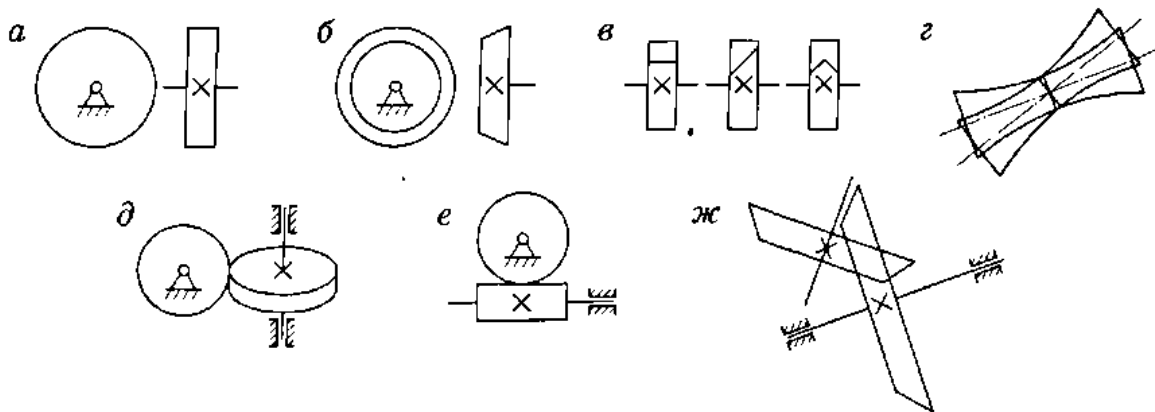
Зубчатые колеса и зубчатые передачи:
